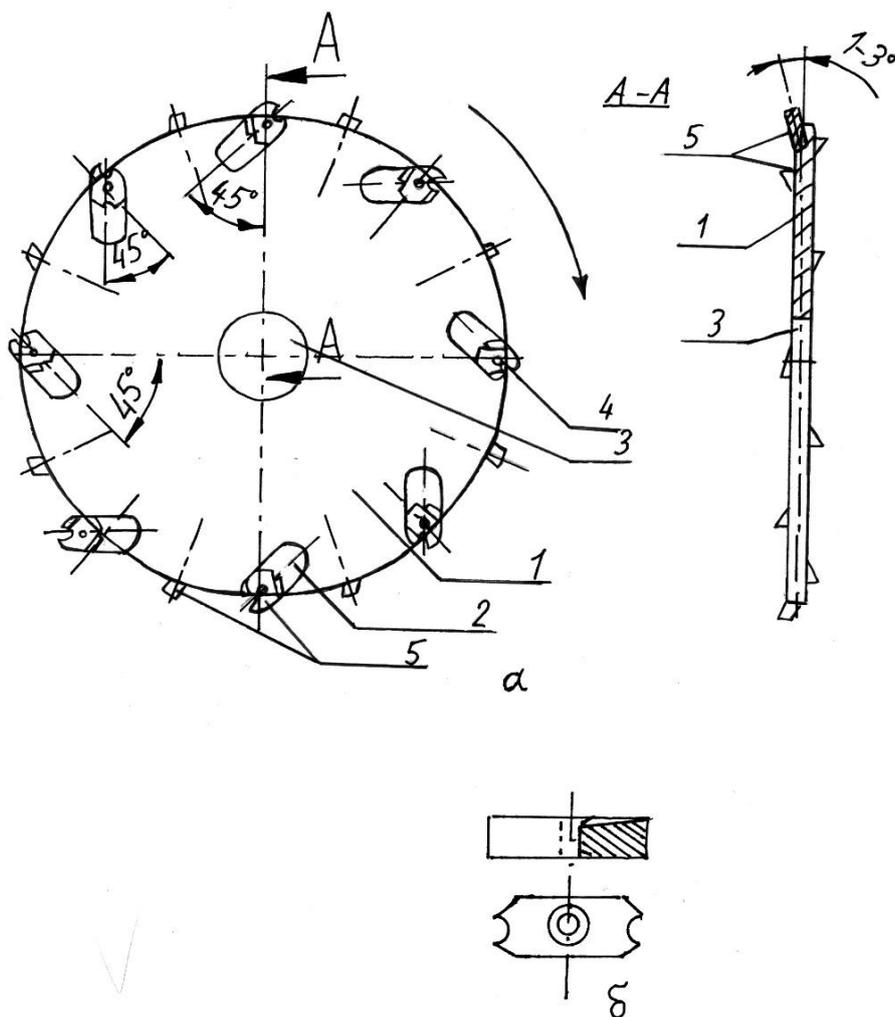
Пила с вставными твердосплавными, поворотными пластинами: а - пила; б – пластина.
